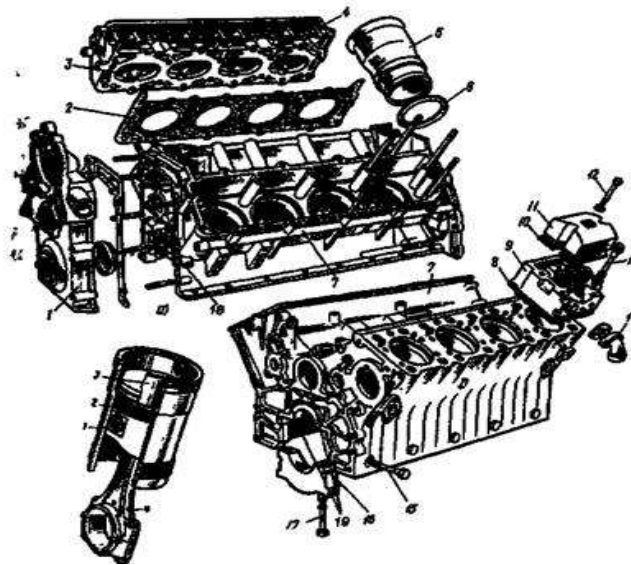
Нерухома частина кривошипно-шатунного механізму
